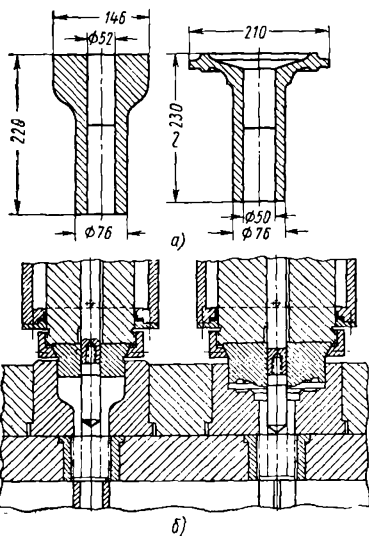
Переходы и схема двухручьевого штамповки поковки со сквозным отверстием: а — переходы штамповки; б — схема штампа
